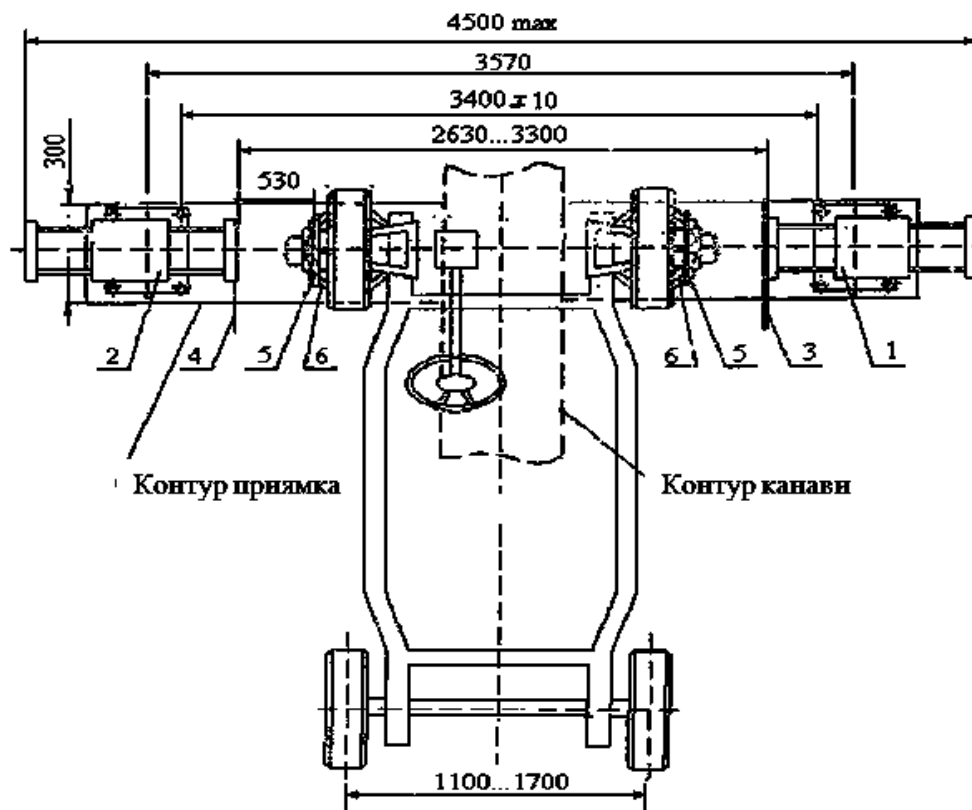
Схема станда: 1 – стійка лазерна права; 2 – стійка лазерна ліва; 3 – шкала права; 4 – шкала ліва; 5 – розпірна консоль; 6 – поворотна платформа
